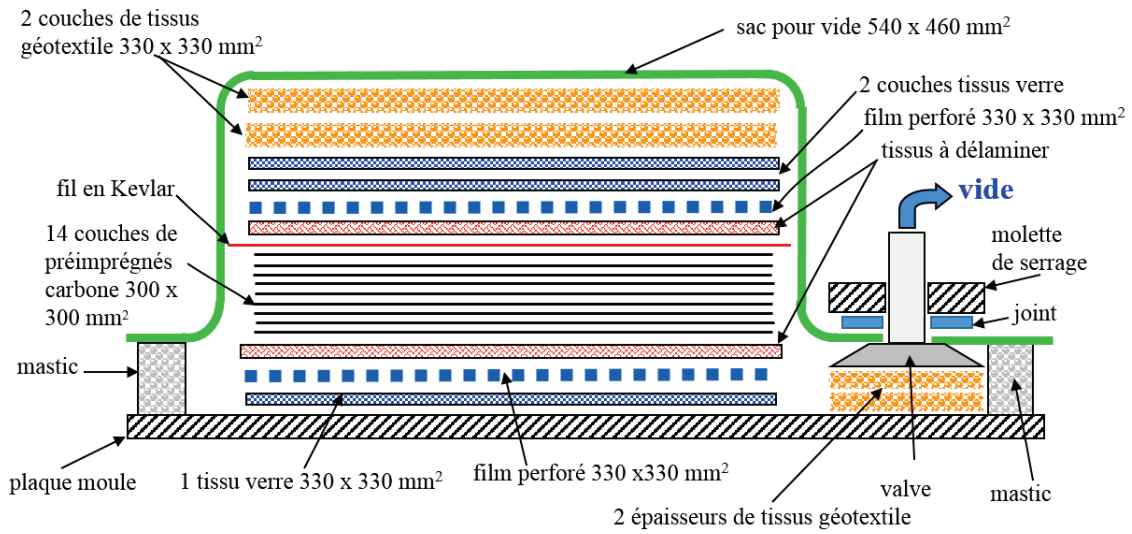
Procédé de fabrication des éprouvettes
